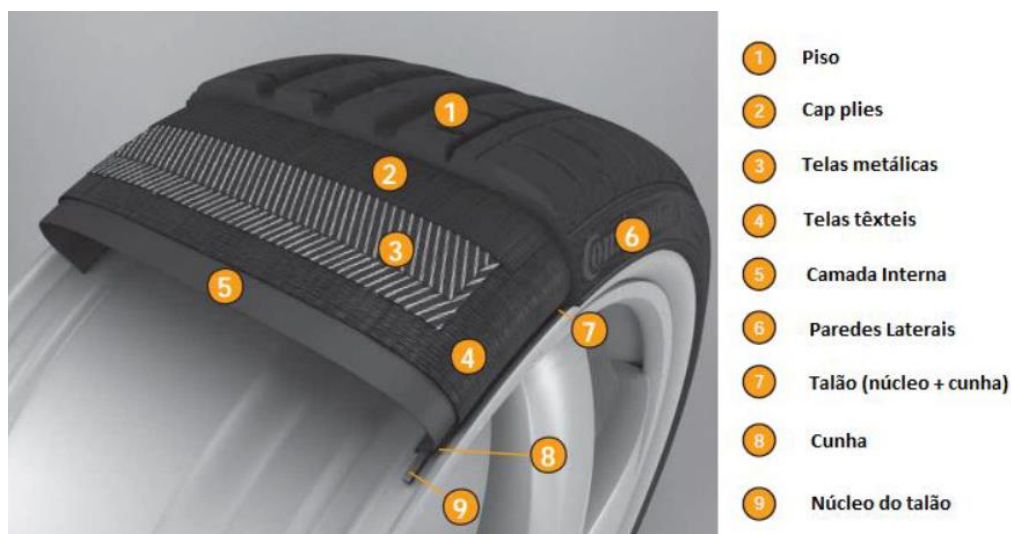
Principais elementos que integram a estrutura geral de um pneu[12]
